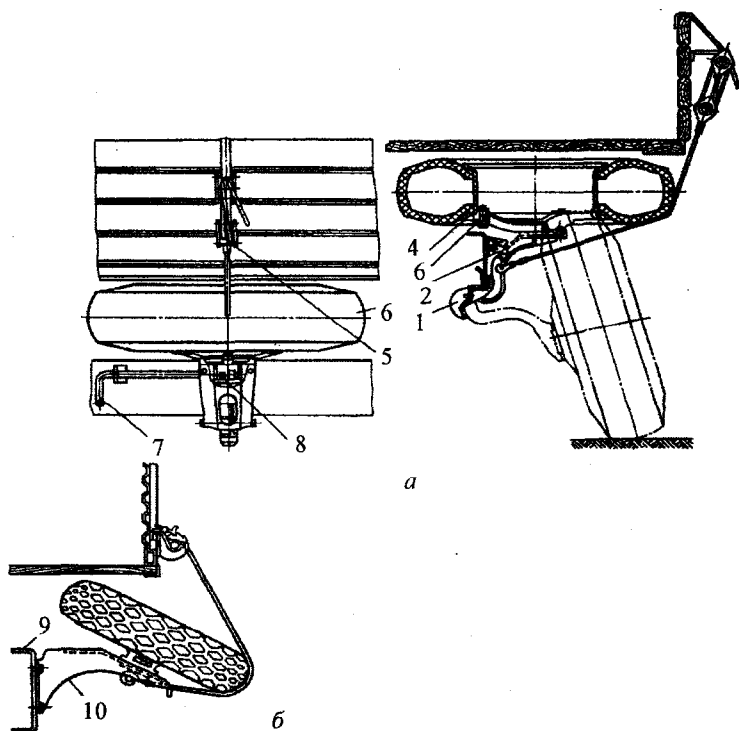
Способы крепления запасного колеса грузовых автомобилей
